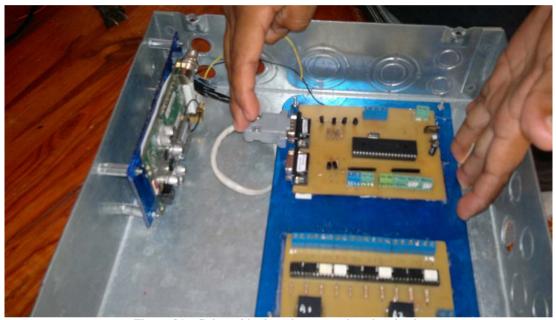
Colocación de tarjetas en caja galvanizada Fuente: Autores
